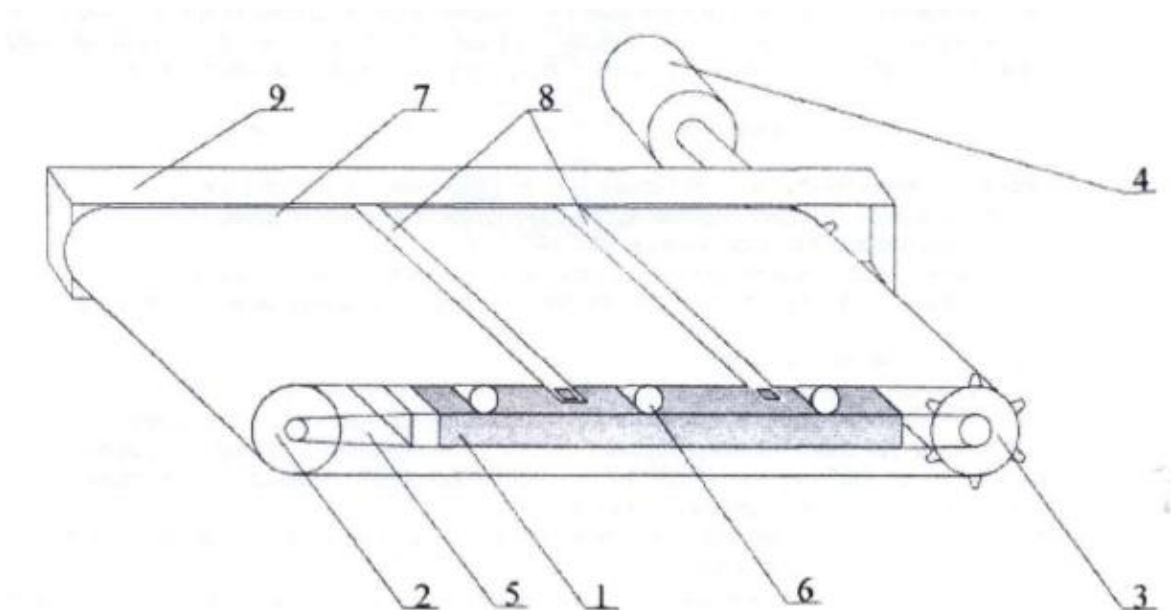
Стрічковий конвеєр для важких вантажів, що забезпечує центральний рух стрічки, де: 1 - рама; 2 - натяжний барабан; 3 - привідний барабан; 4 - привід; 5 - вузол натягування; 6 - опорні ролики; 7 -
